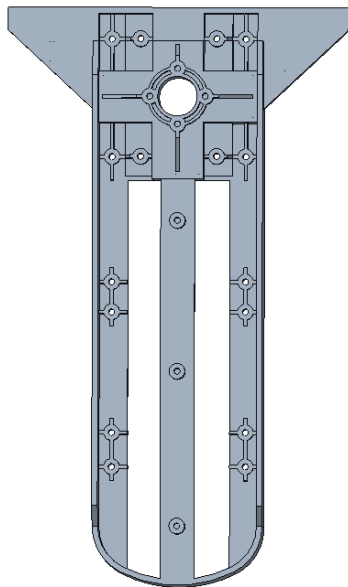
Columna media con los dos planos de atornillado (frontal).
